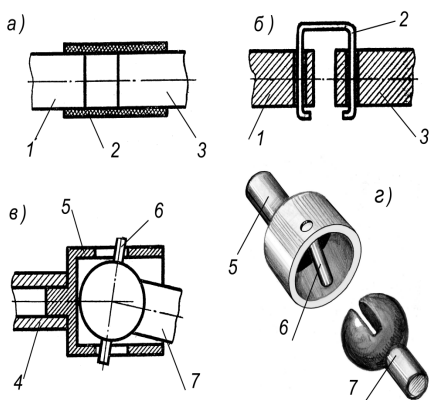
Конструкції муфт з різними сполучними елементами: 1 – ведений вал; 2 – сполучний елемент; 3 – ведучий вал; 4 – м'який сполучний елемент; 5 – корпус шарнірного з'єднання; 6 – елемент, що передає обертальний момент; 7 – ведучий елемент шарнірного з'єднання.
